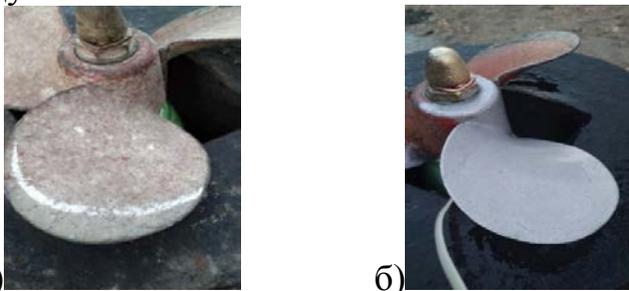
Внешний вид лопастей гребного винта: а – поверхность до обработки; б – обработанная поверхность
